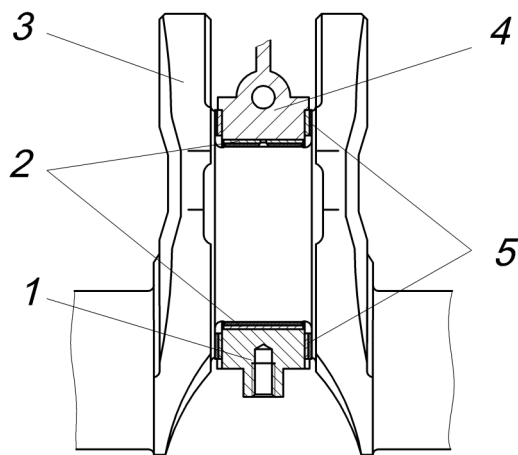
Средний коренной подшипник коленчатого вала:
